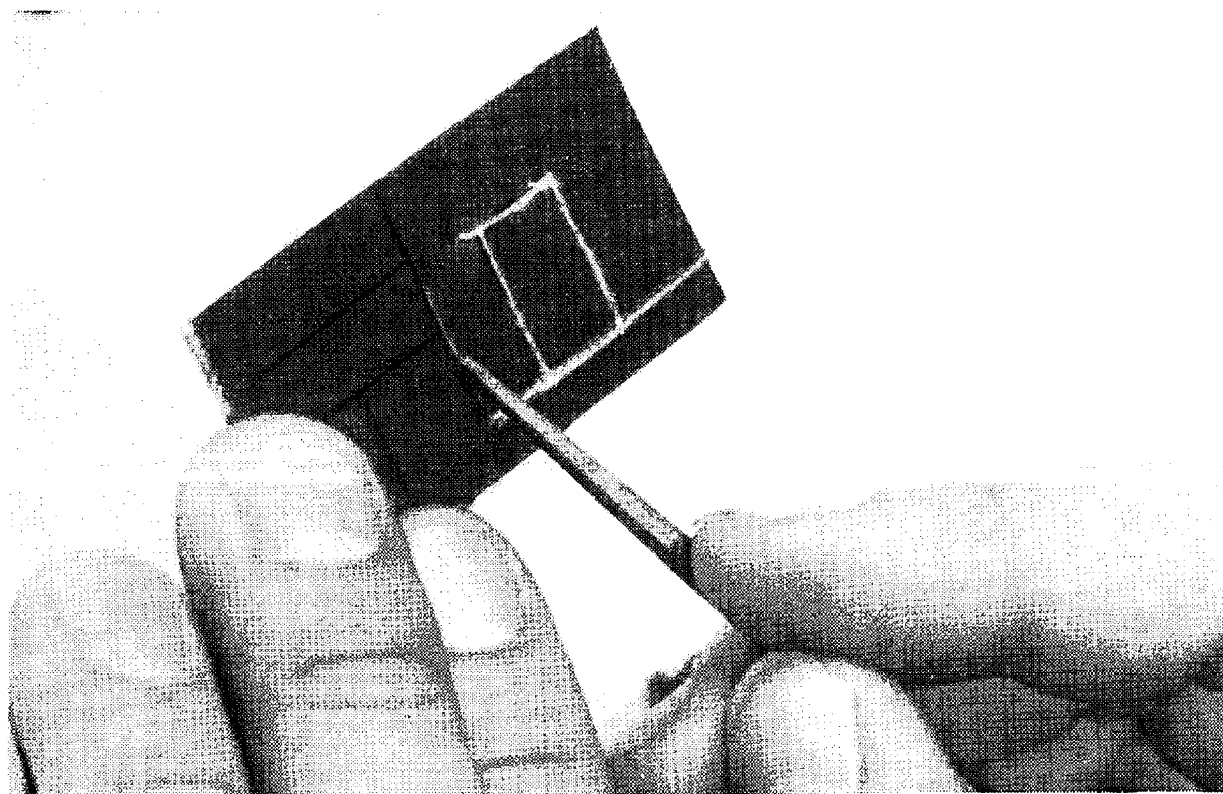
Přenesení obrazce plošných spojů na cuprexit pomocí uhlového papíru při zhotovování prototypu
